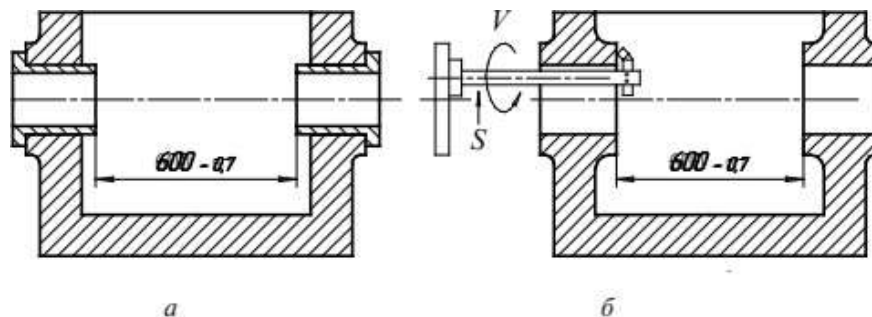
Конструкція корпусних деталей з точним розміром між внутрішніми торцями отворів:
